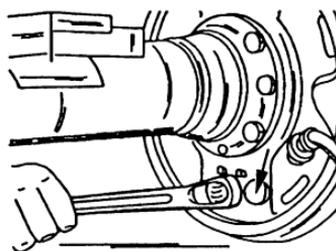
Болт крепления регулировочного механизма фирмы Perrot (стрелкой указано расположение пробки регулировочного отверстия)
